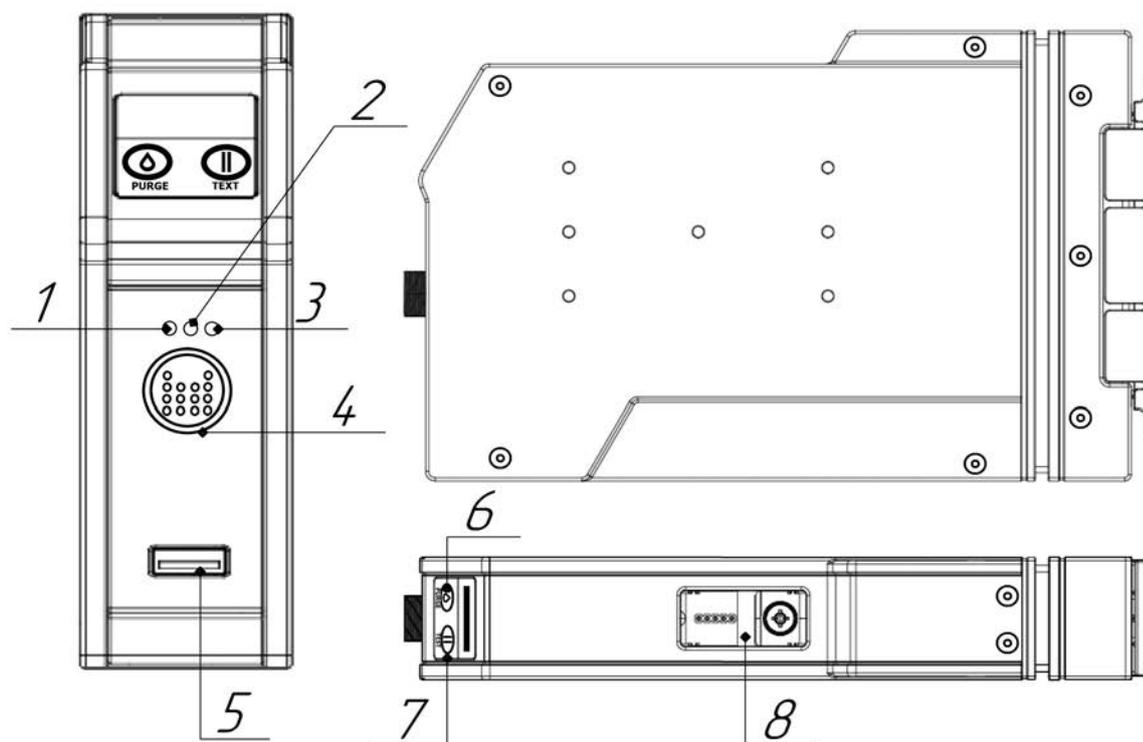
Внешний вид боковых поверхностей печатающих головок типов 8В и 8С.
